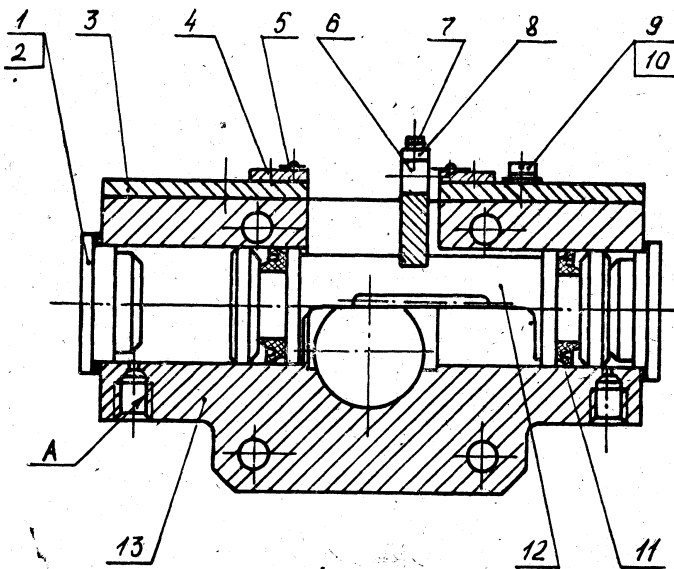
Механізм повороту: 1 – фланець; 2 – прокладка; 3 – планка; 4 – плата; 5 – магнітокерований контакт (КЕМ); 6 – магніт; 7 – гвинт; 8 – планка; 9 – гвинт; 10 – шайба пружинна; 11 – манжета; 12 – рейка; 13 – корпус.
